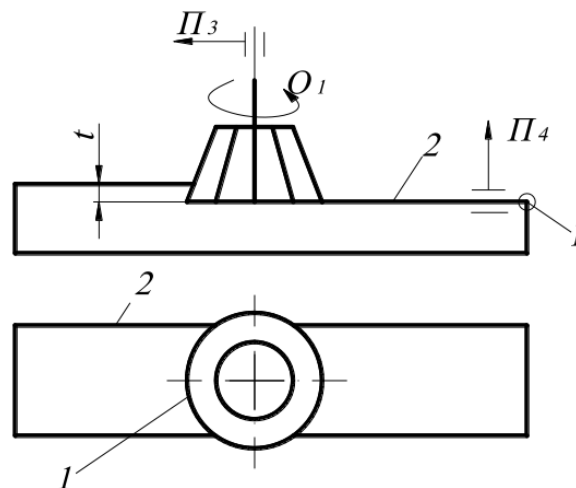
Обробка плоскої поверхні торцевою фрезою
